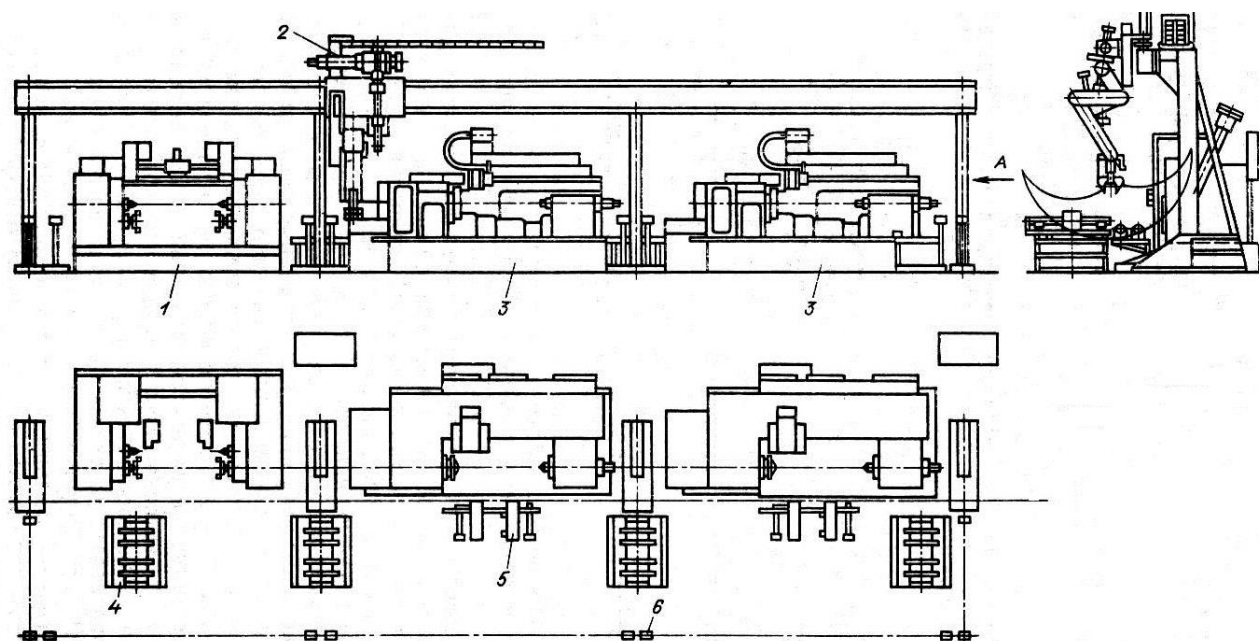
Багатопозиційні РТК на базі токарних верстатів
